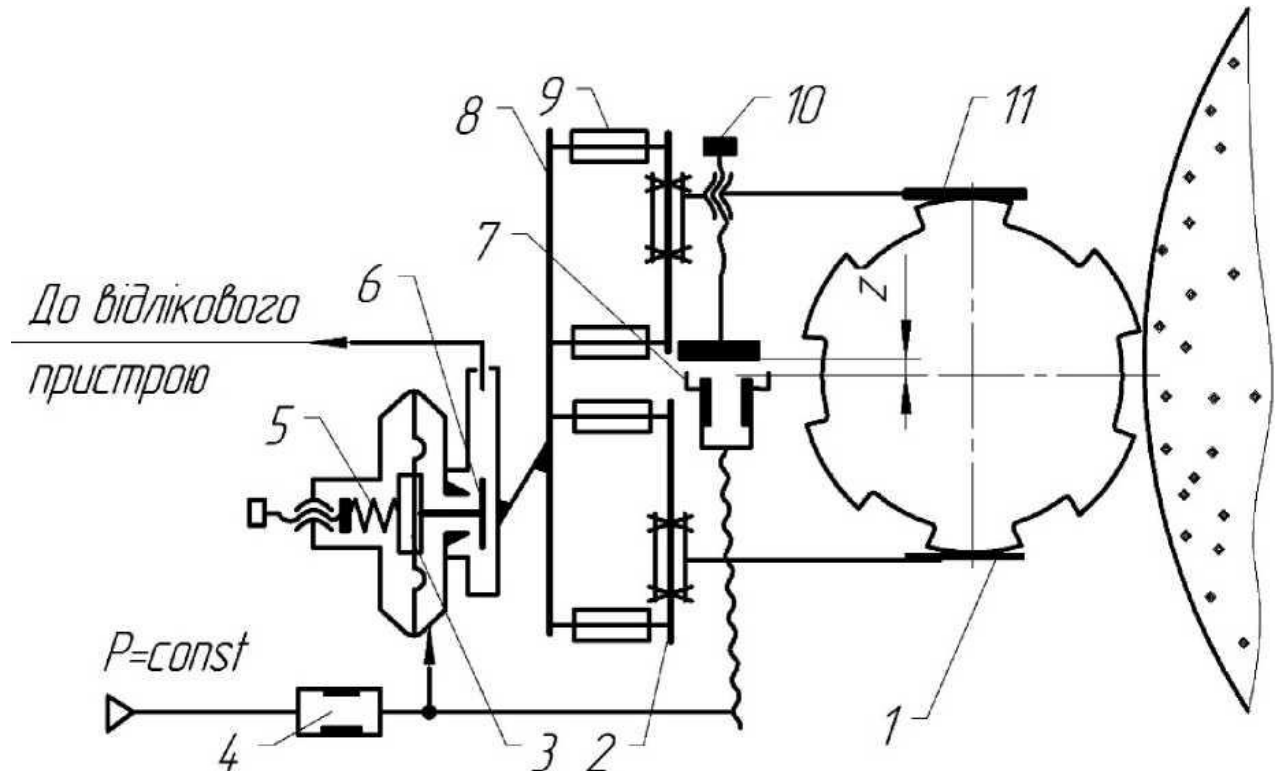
Вимірювальний пристрій з блокувальним клапаном
